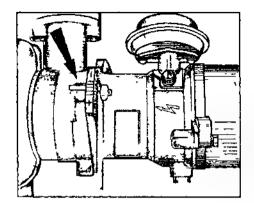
Установка датчика-распределителя (стредкей показан установочный выступ на корпусе вспомогательных агрегатов)
